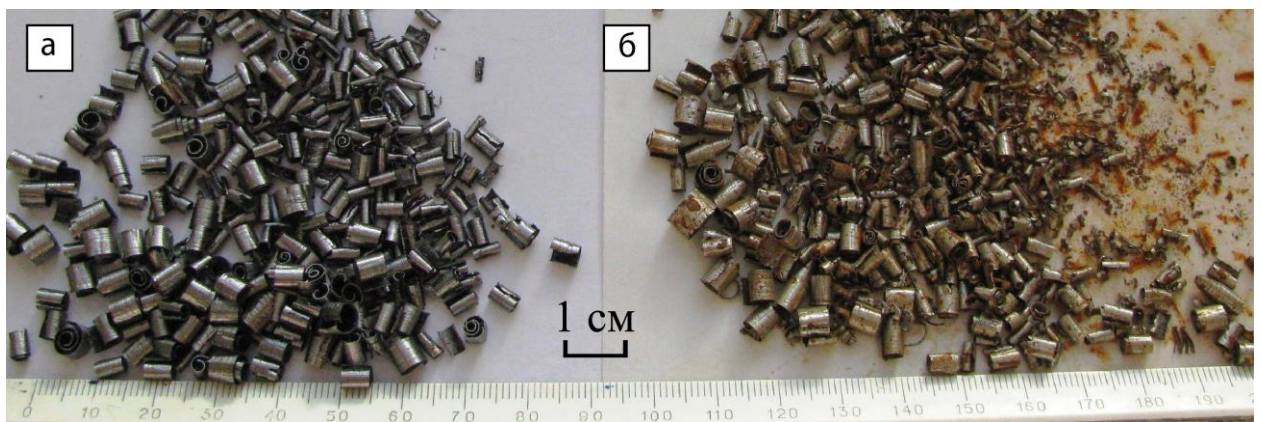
Вигляд стружки, що утворилась під час механічної обробки:
